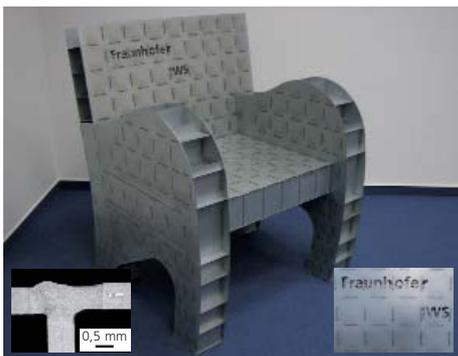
Demonstrator: laserstrahlgeschweißte Steg-Schlitz Konstruktion aus verzinktem Blech
